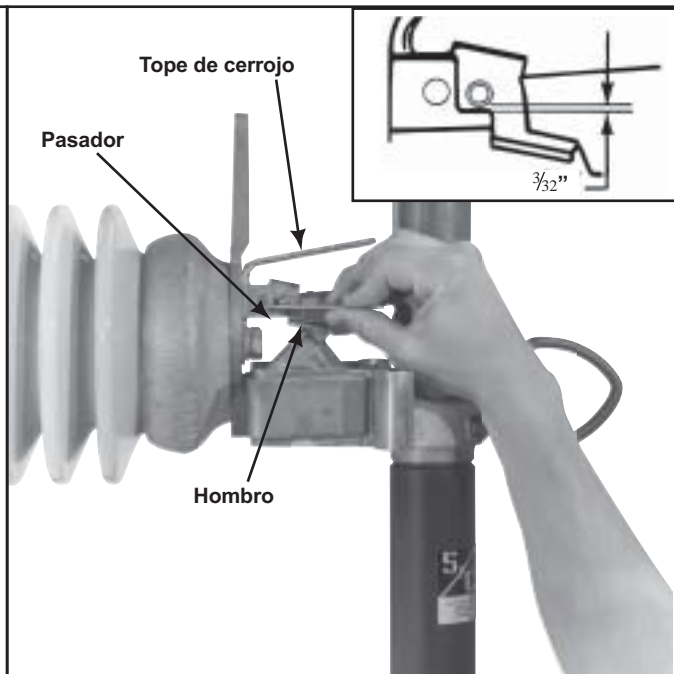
Revisión de la separación entre el pasador del conjunto de enganche y la pieza fundida de contacto del hombro.
